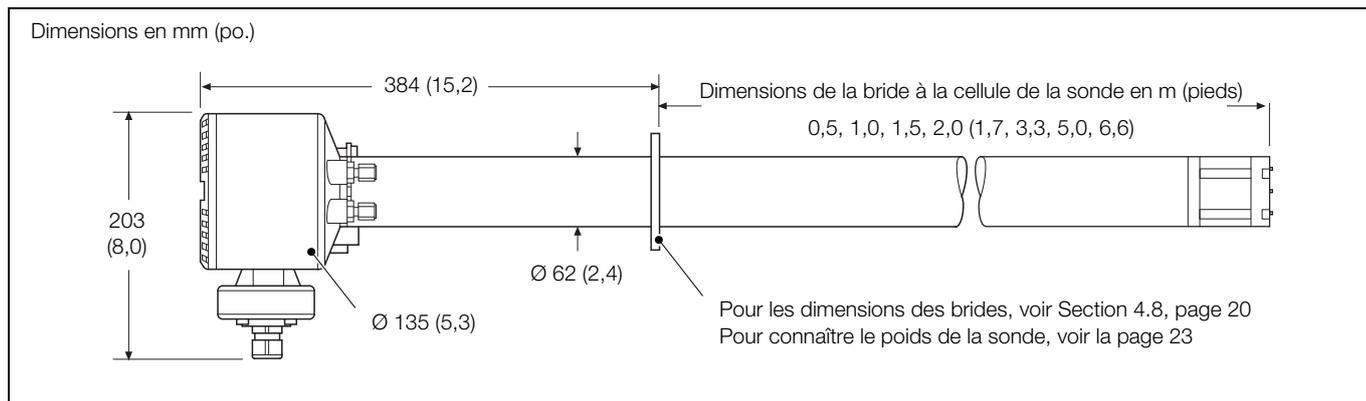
Dimensions générales – Sonde Endura AZ30 déportée
